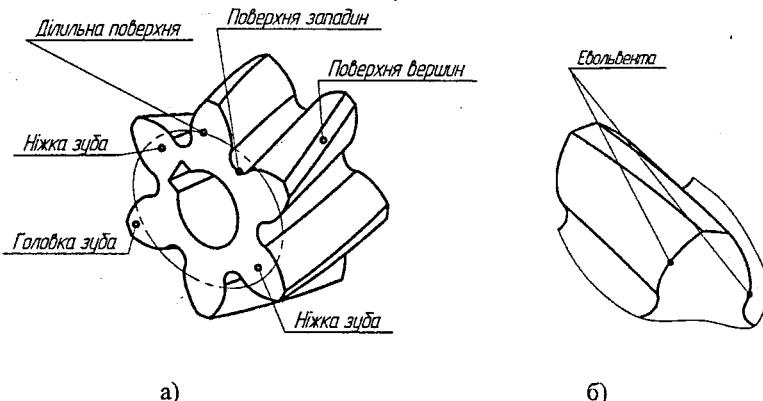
Елементи (*components*) евольвентного зубчастого колеса
